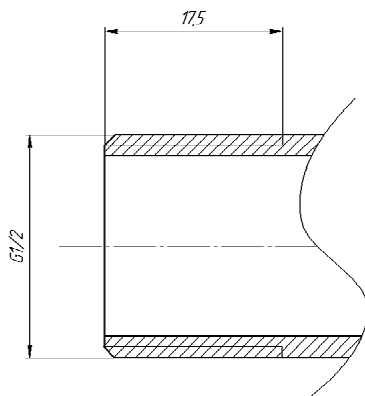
Присоединительные размеры патрубка рубашки обогрева
